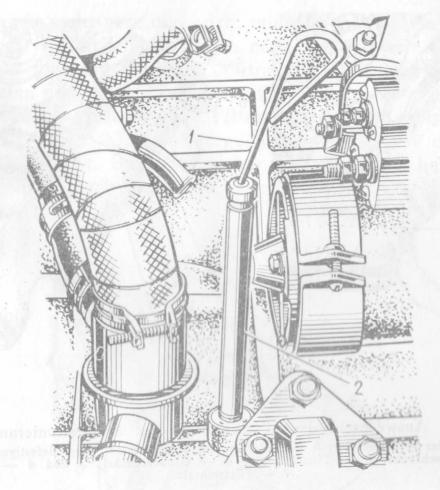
Anordnung des Ölmeßstabes: 1 — Olmeßstab; 2 — Führungsrohr
